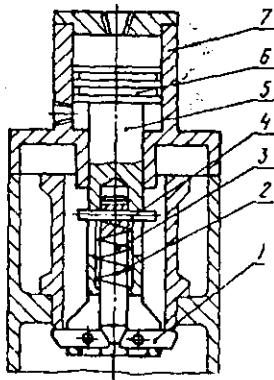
4. Приспособление для снятия гильзы цилиндра: 1—захват; 2—пружина; 3—клин; 4—штифт; 5—шток; 6—поршень; 7—гидроцилиндр.
